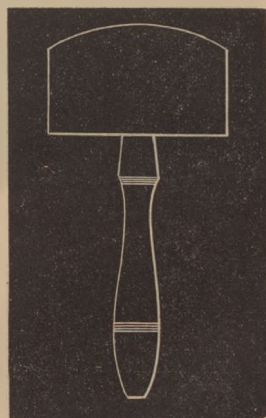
Werkzeugklöpfel aus Birkenholz.
